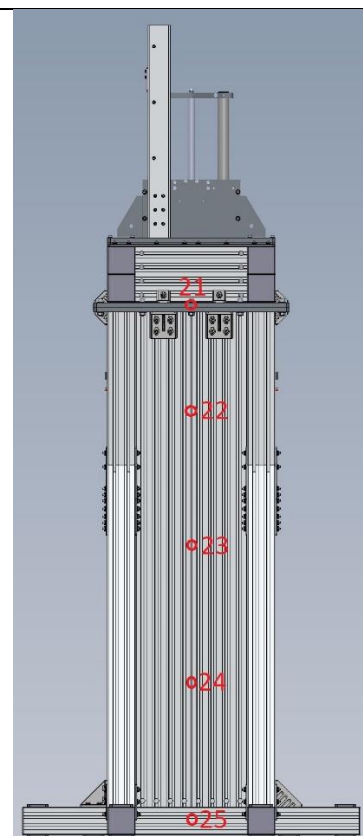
Posiciones vista derecha. Fuente: Elaboración propia
